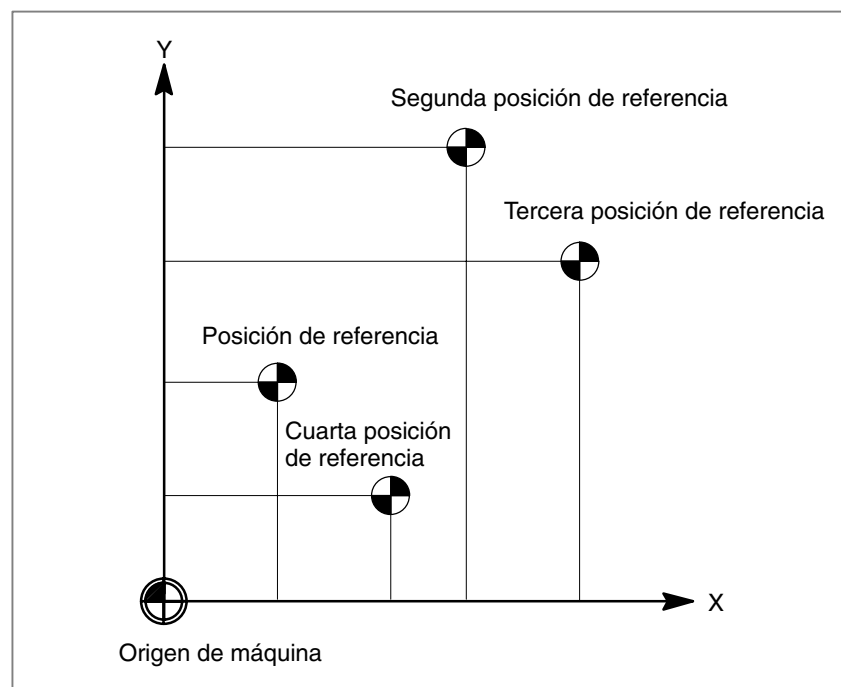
(a) Origen de máquina y posiciones de referencia
